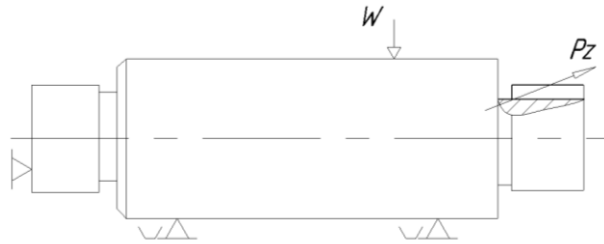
Схема закріплення в пристосуванні для фрезерування шпонкових пазів
